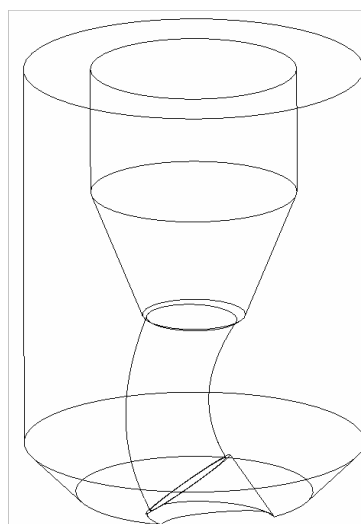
Схема конструкції насадки (відображення каркасне із тонкими невидимими лініями)
